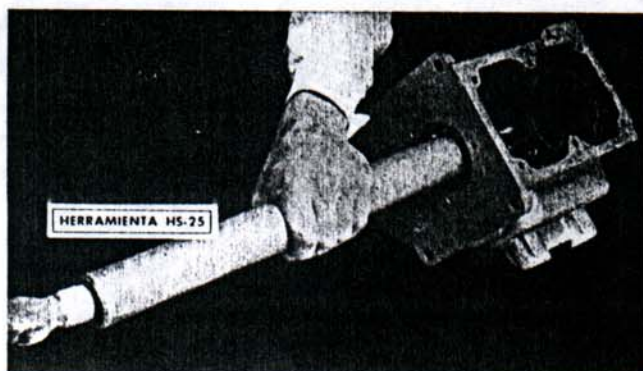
Extrayendo el engranaje de mando, con la herramienta HS-25.
